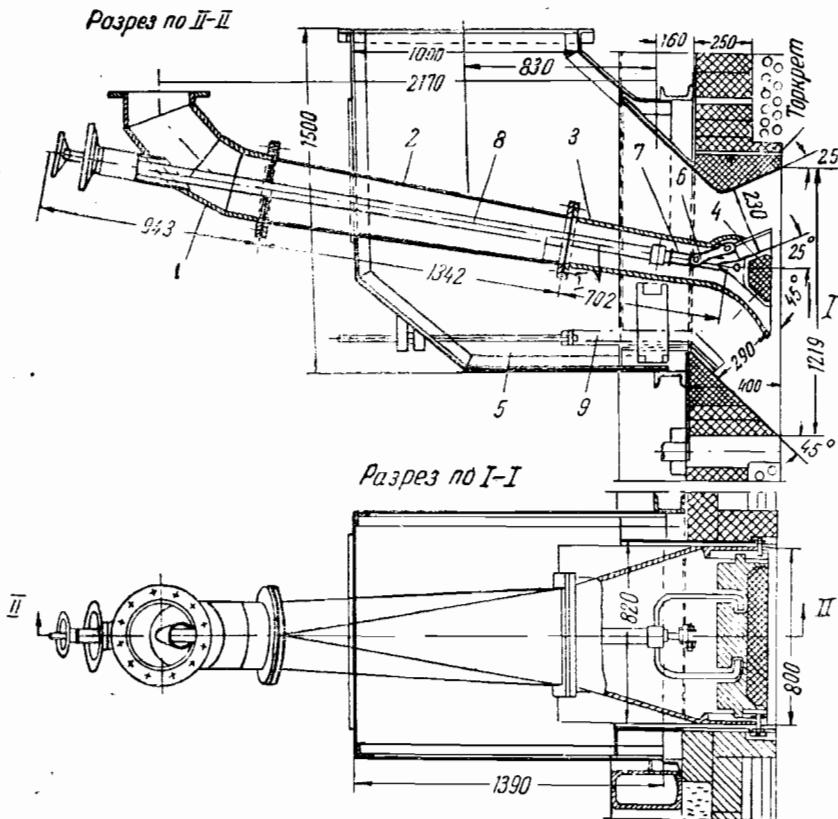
Щелевая горелка Оргрэс-БПК с рассекателем: 1—подводящее колено; 2 — переходной патрубок; 3 — чугунный раструб; 4 — рассекатели; 5 — короб вторичного воздуха; 6 — рычажная передача; 7 — шток; 8 — труба; 9 — шибер
